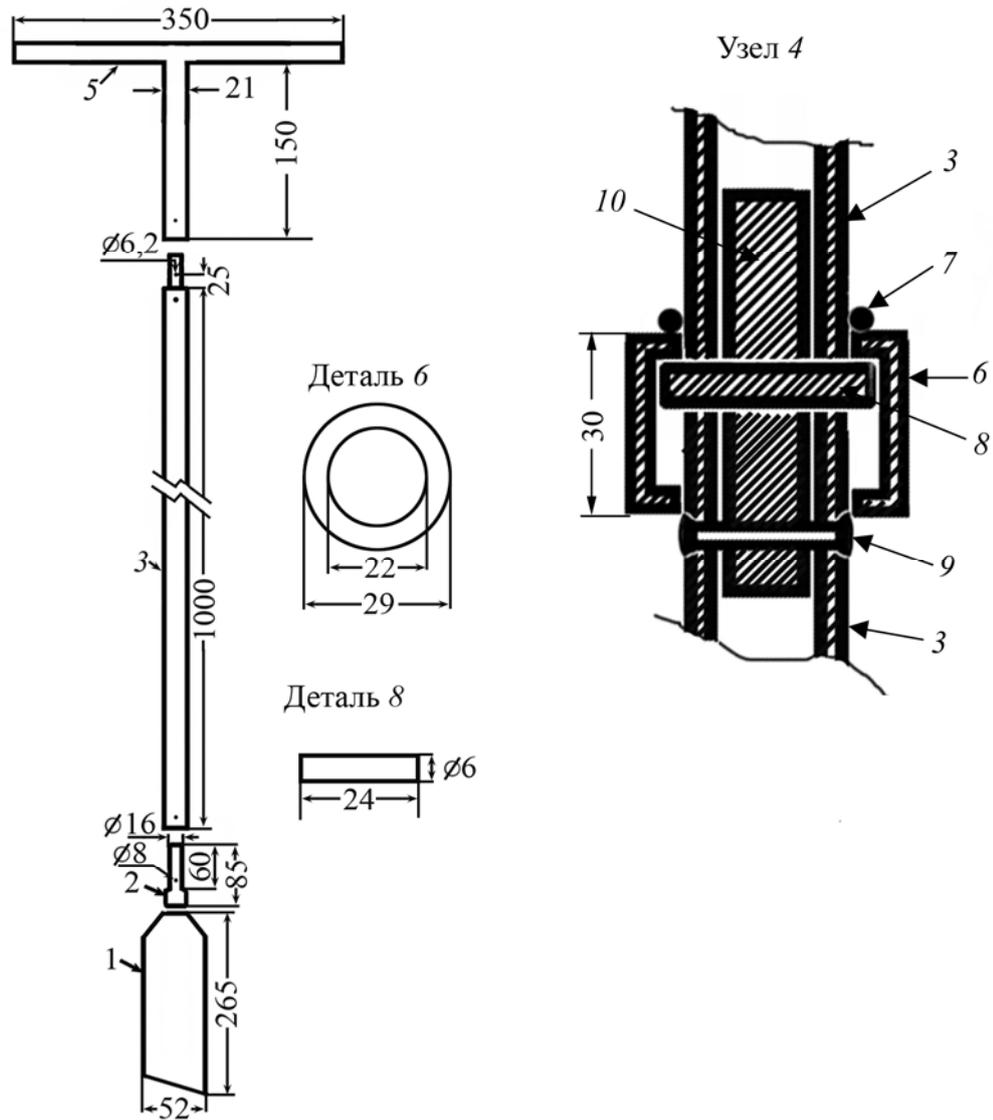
Почвенный бур: 1 – рабочий орган; 2 – переходник; 3 – штанга; 4 – узел соединения штанг; 5 – ручка; 6 – скользящая муфта; 7 – резиновое колечко; 8 – соединительный штырек; 9 – заклепка; 10 – соединительный штырь; размеры указаны в миллиметрах
